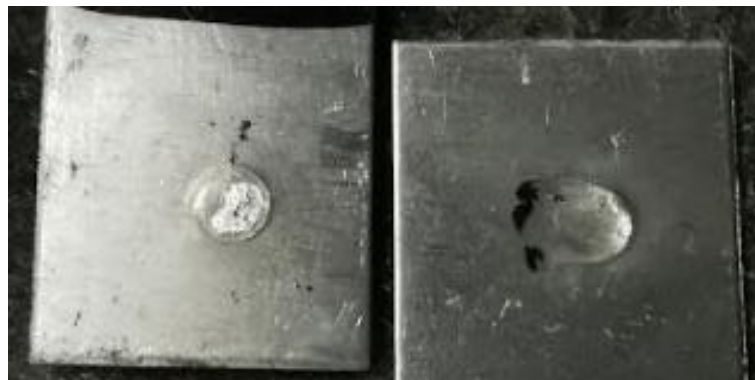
Foto da rotura do ponto de soldadura proveniente do ensaio de corte no provete 3E fabricado em alumínio 1050 (zona interna – esquerda; zona externa – direita)
